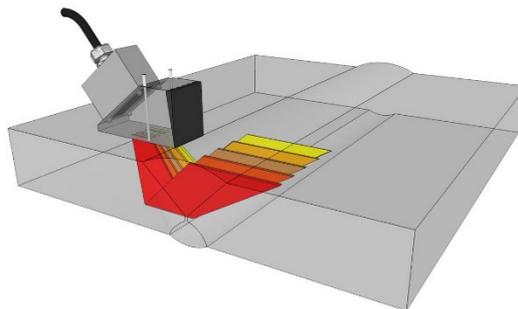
2D-Schallbündelschwenk. Bei 64 parallelen Kanälen kann mit Matrix-Prüfköpfen das Schallfeld auch seitlich geschwenkt werden. Hiermit wird die Fehlerrückmeldung bei der Schweißnahtprüfung deutlich erhöht.
